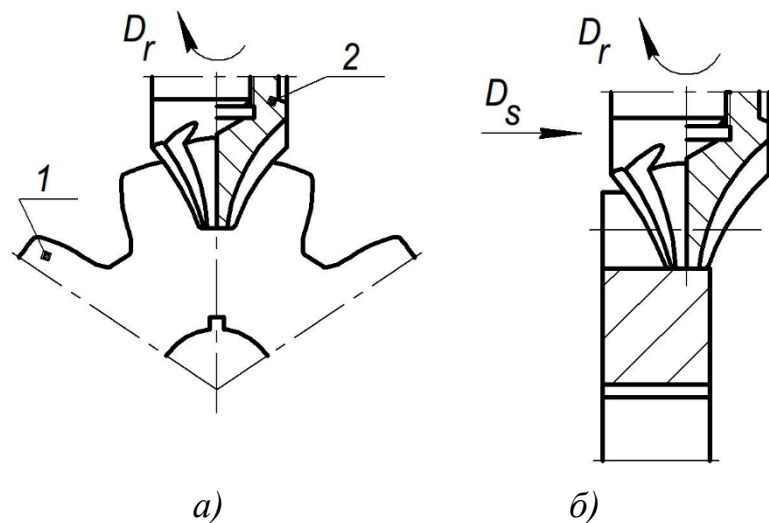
Схема оброблення зуба колеса пальцевою модульною фрезою:
